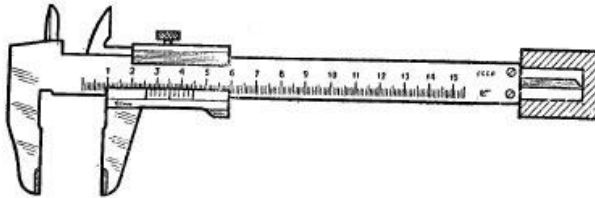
Положение линейки глубиномера относительно проверяемой детали
